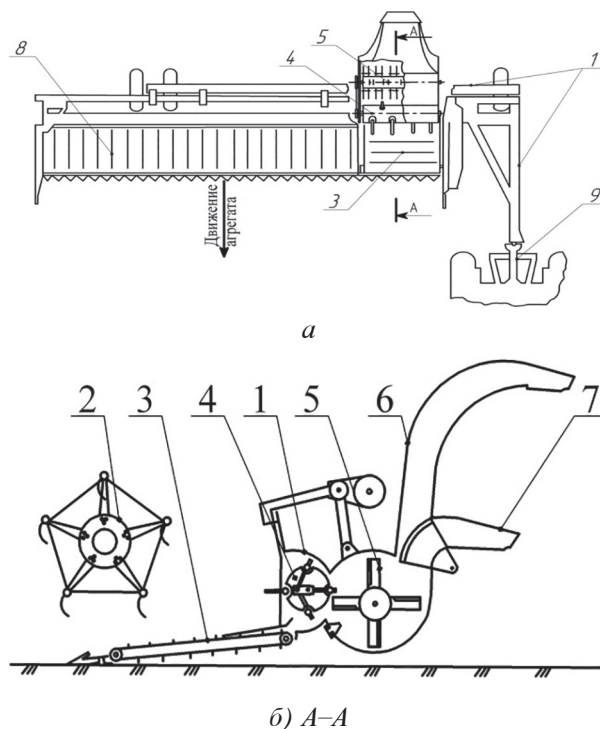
Прицепной жатвенный агрегат на базе прицепного адаптера для измельчения очесанного стеблестоя, его разбрасывания по полю или загрузки в транспортное средство:
